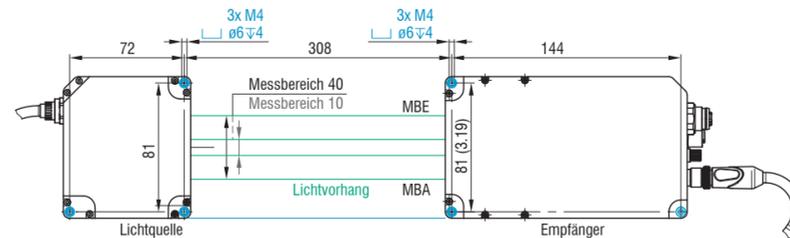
Montagegewinde für Direktverschraubung ODC2700-10, ODC2700-40., Abmessungen in mm
